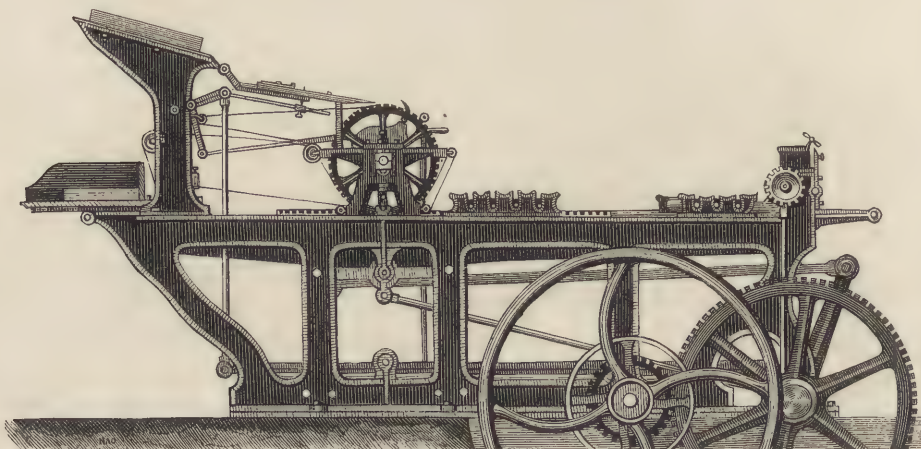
Vue en profil de la machine en blanc Dutartre.
